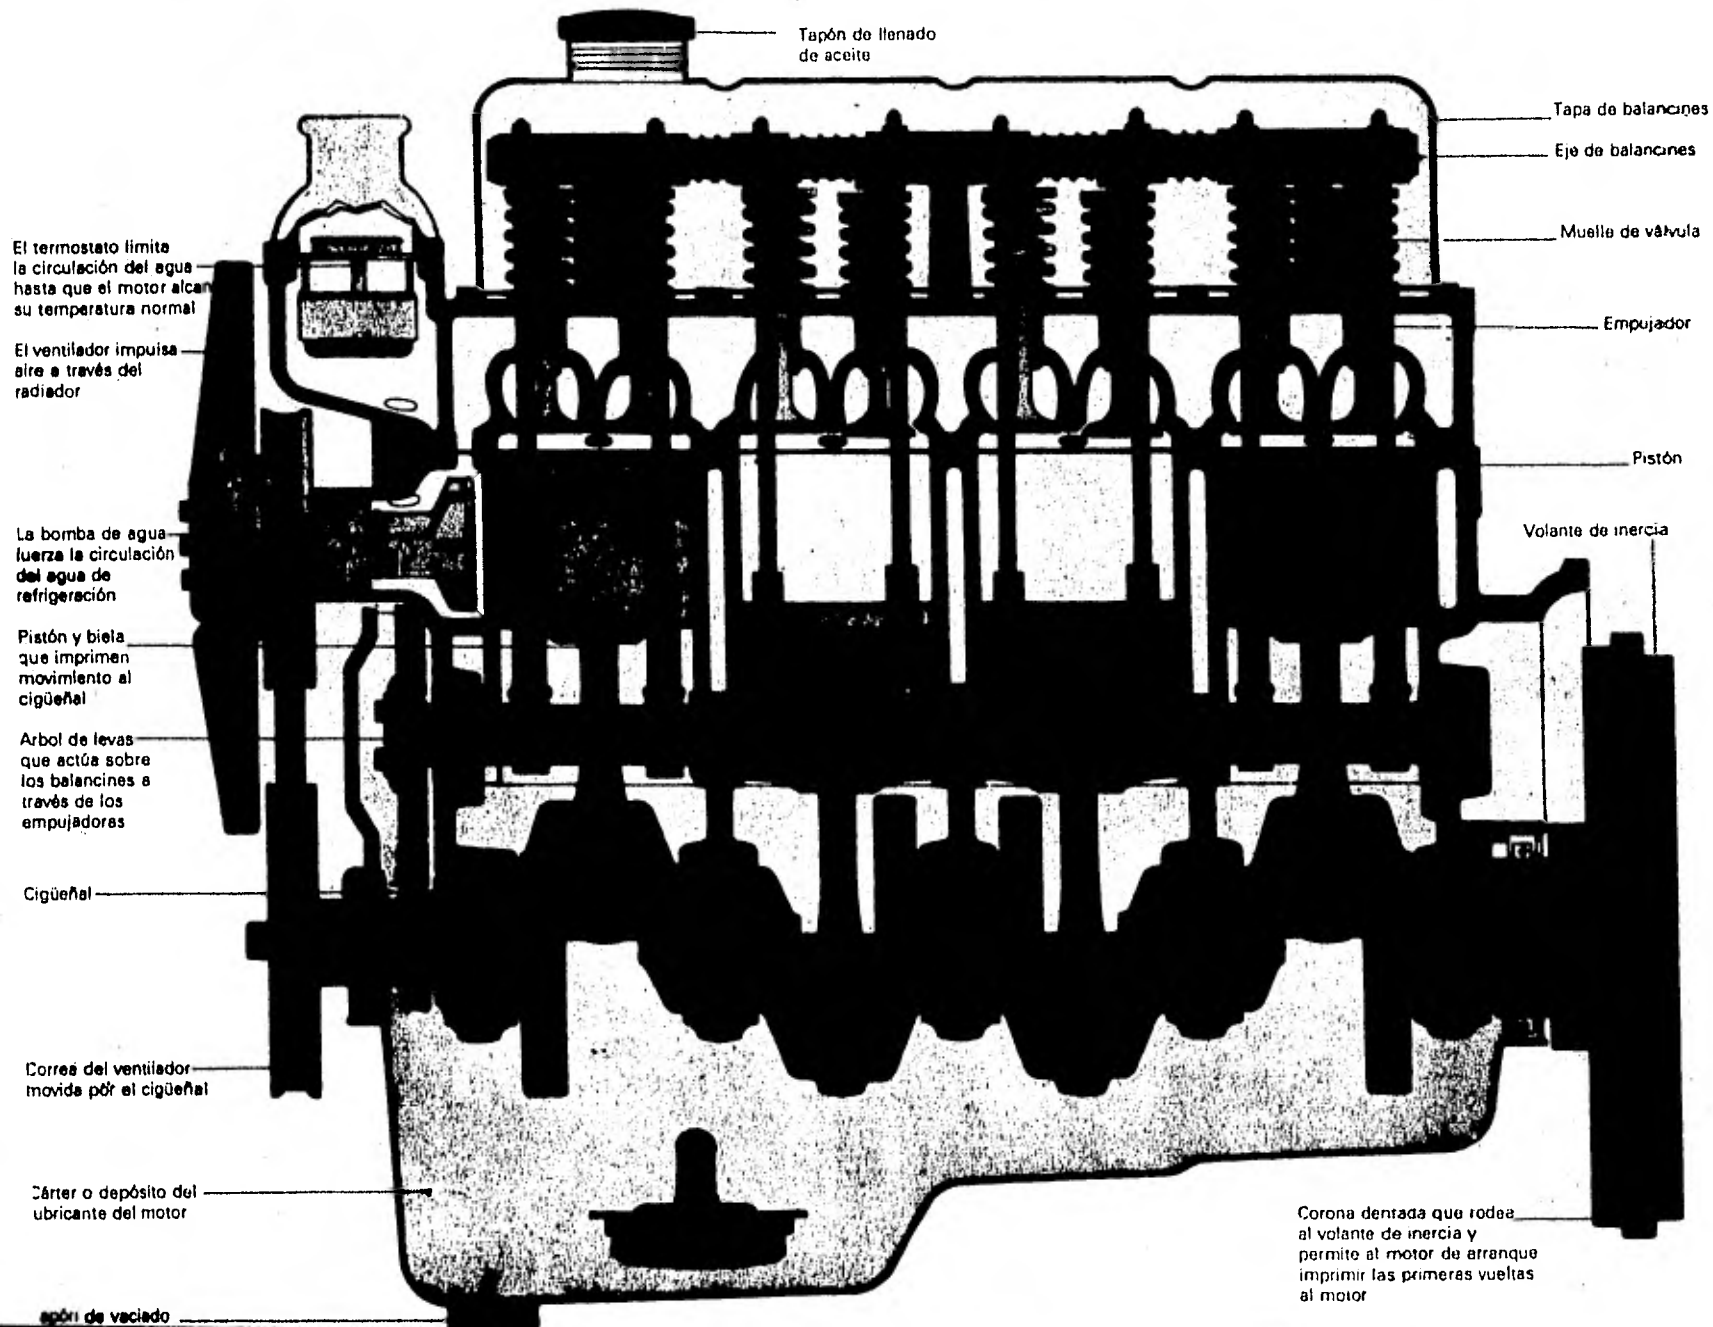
SECCION LATERAL DE UN MOTOR DE EXPLOSION DE 4 CILINDROS
